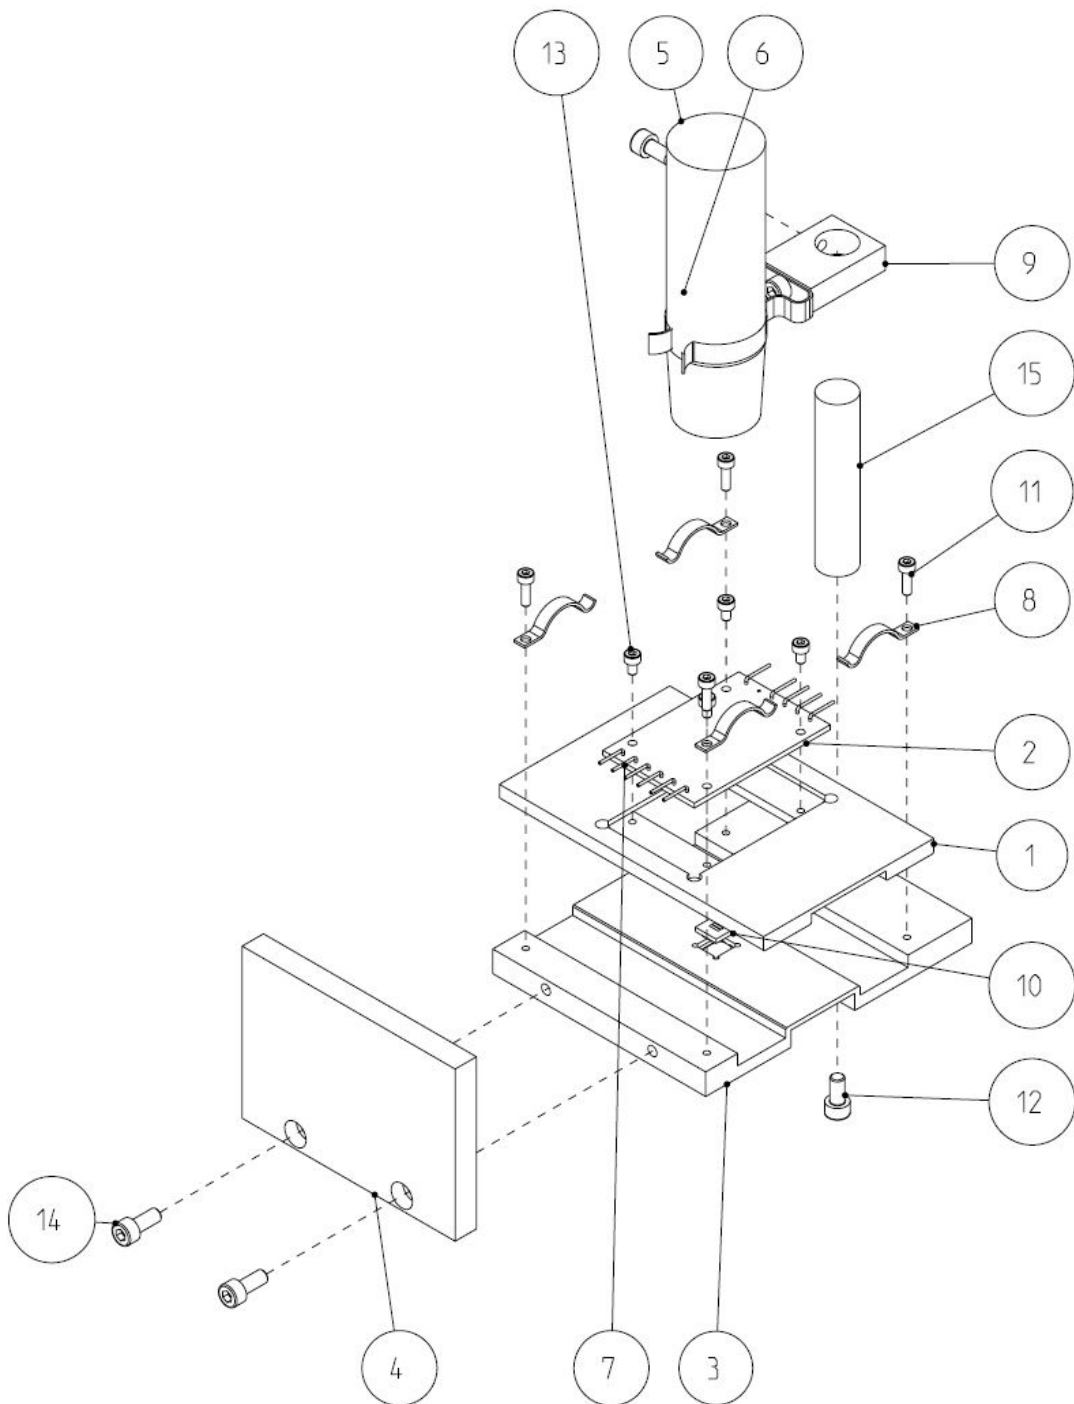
Explosionsansicht der Optik-Messzelle mit Kamerahalterung⁷⁰
